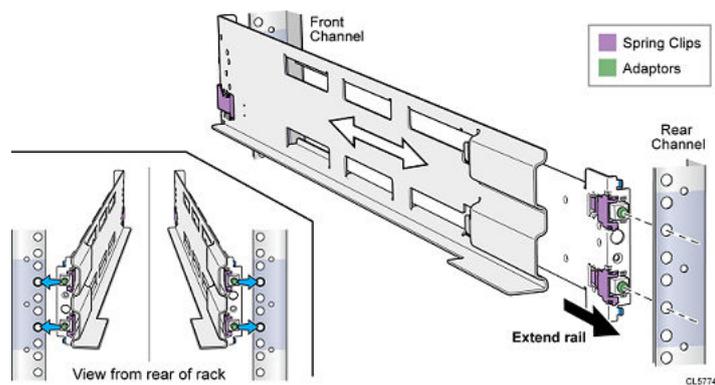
Drücken Sie die Schiene in die Montagelöcher der hinteren Führung.
